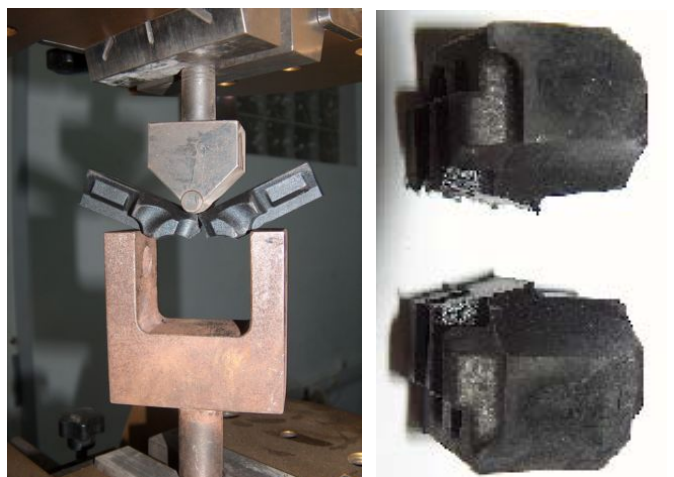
Fractura de la línea de soldadura mediante ensayo de flexión
